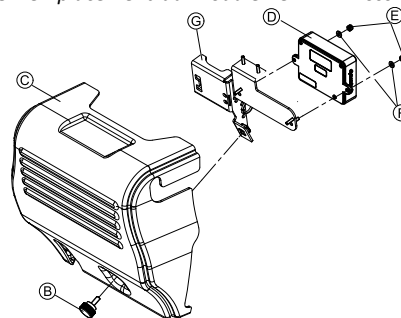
Remplacement du module vérin — Dossier électrique
